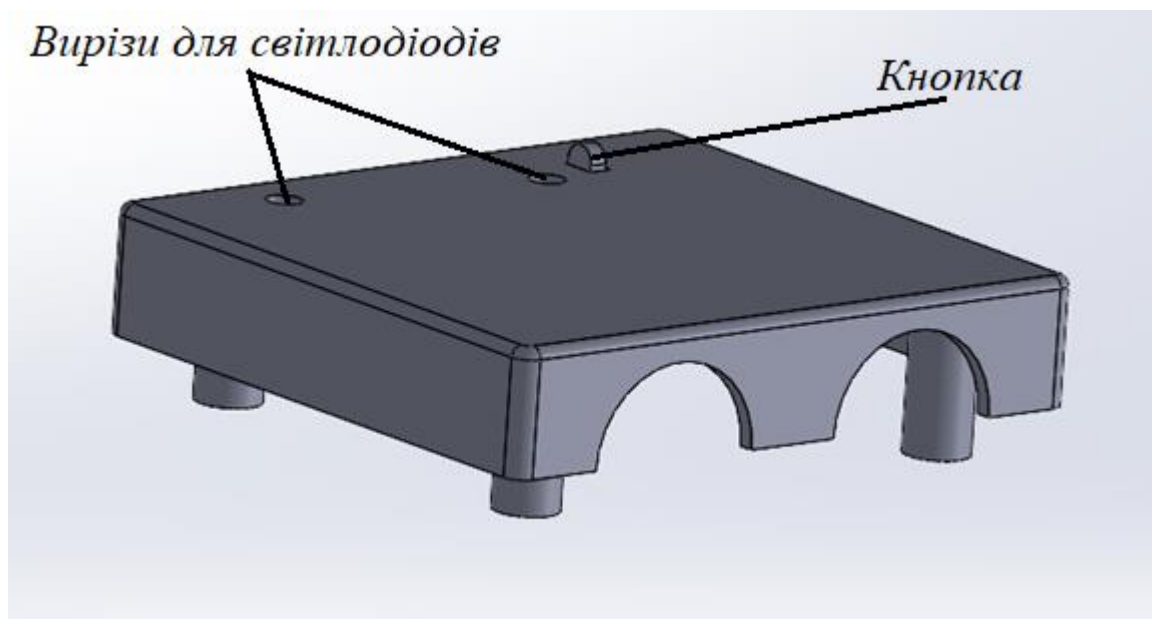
3Д модель верхньої частини корпусу.
